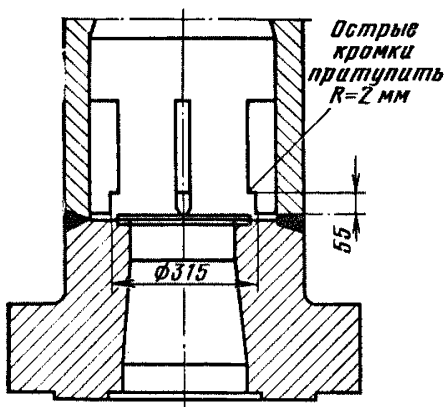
Расточка направляющих ребер в корпусе обратного клапана ЛМЗ.
